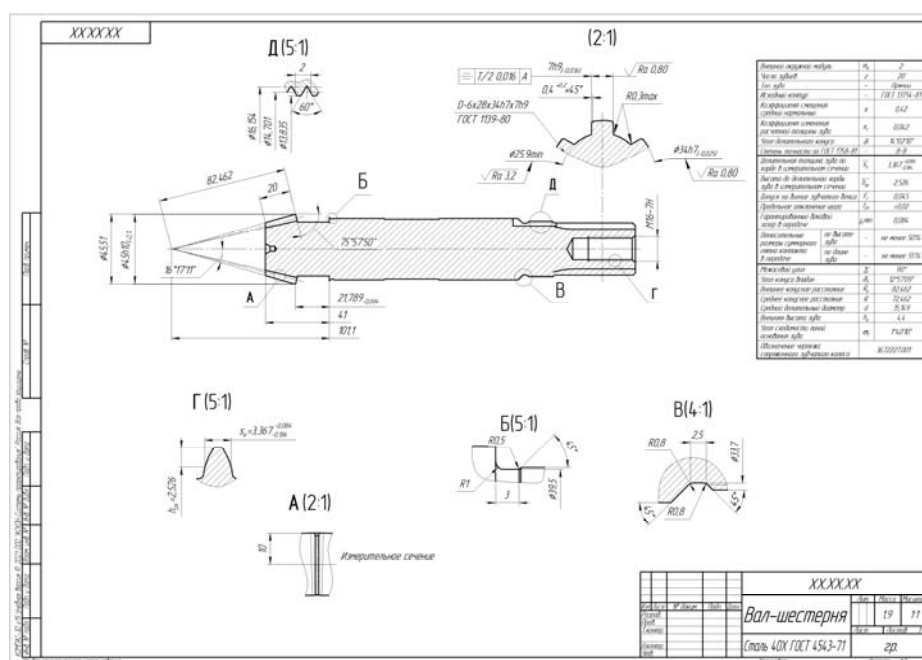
Чертеж модели «Вал – шестерня»
